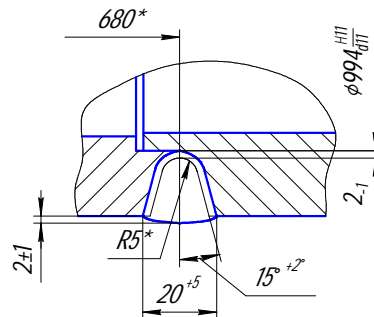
Схема стикового зварного з'єднання С20, шов №3,4
